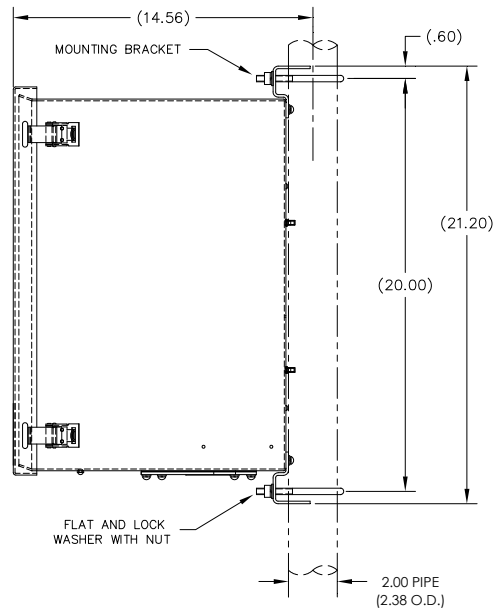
Instalação do invólucro 6700 no tubo de fixação
